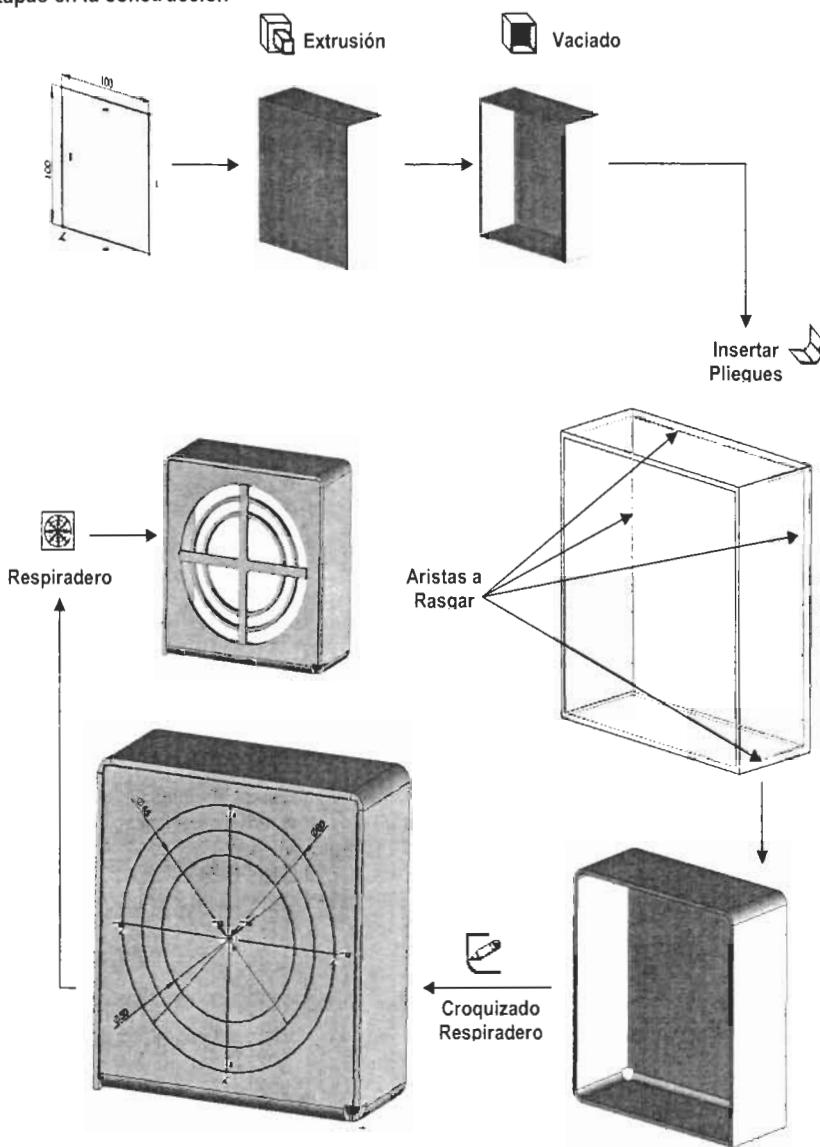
Etapas en la construcción del modelo de Chapa Metálica.
